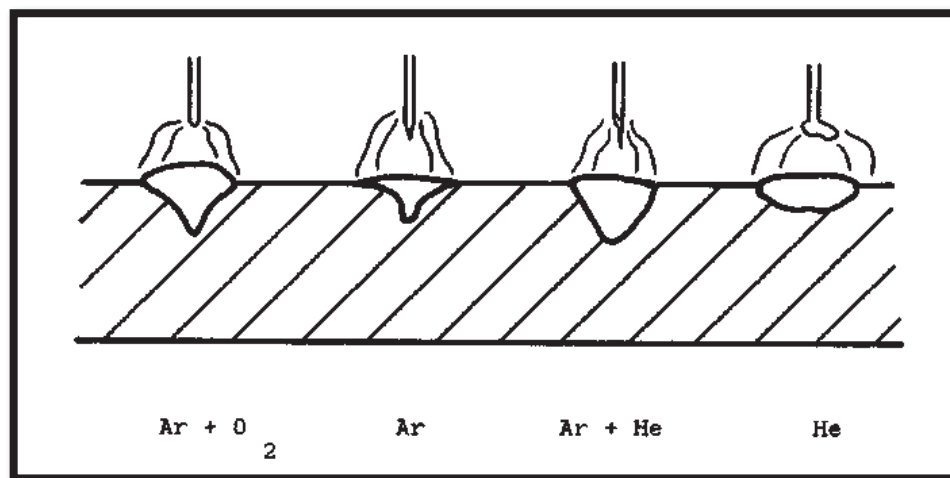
Forma de la soldadura en función del gas.
